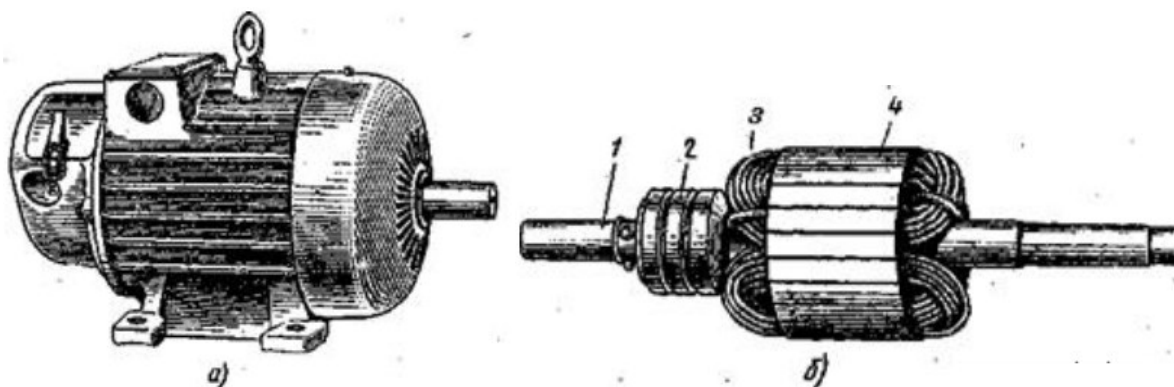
Асинхронный электродвигатель с фазным ротором: а — общий вид, б — ротор; 1 — вал, 2 — контактные кольца, 3 — обмотка ротора, 4 — пакет ротора
